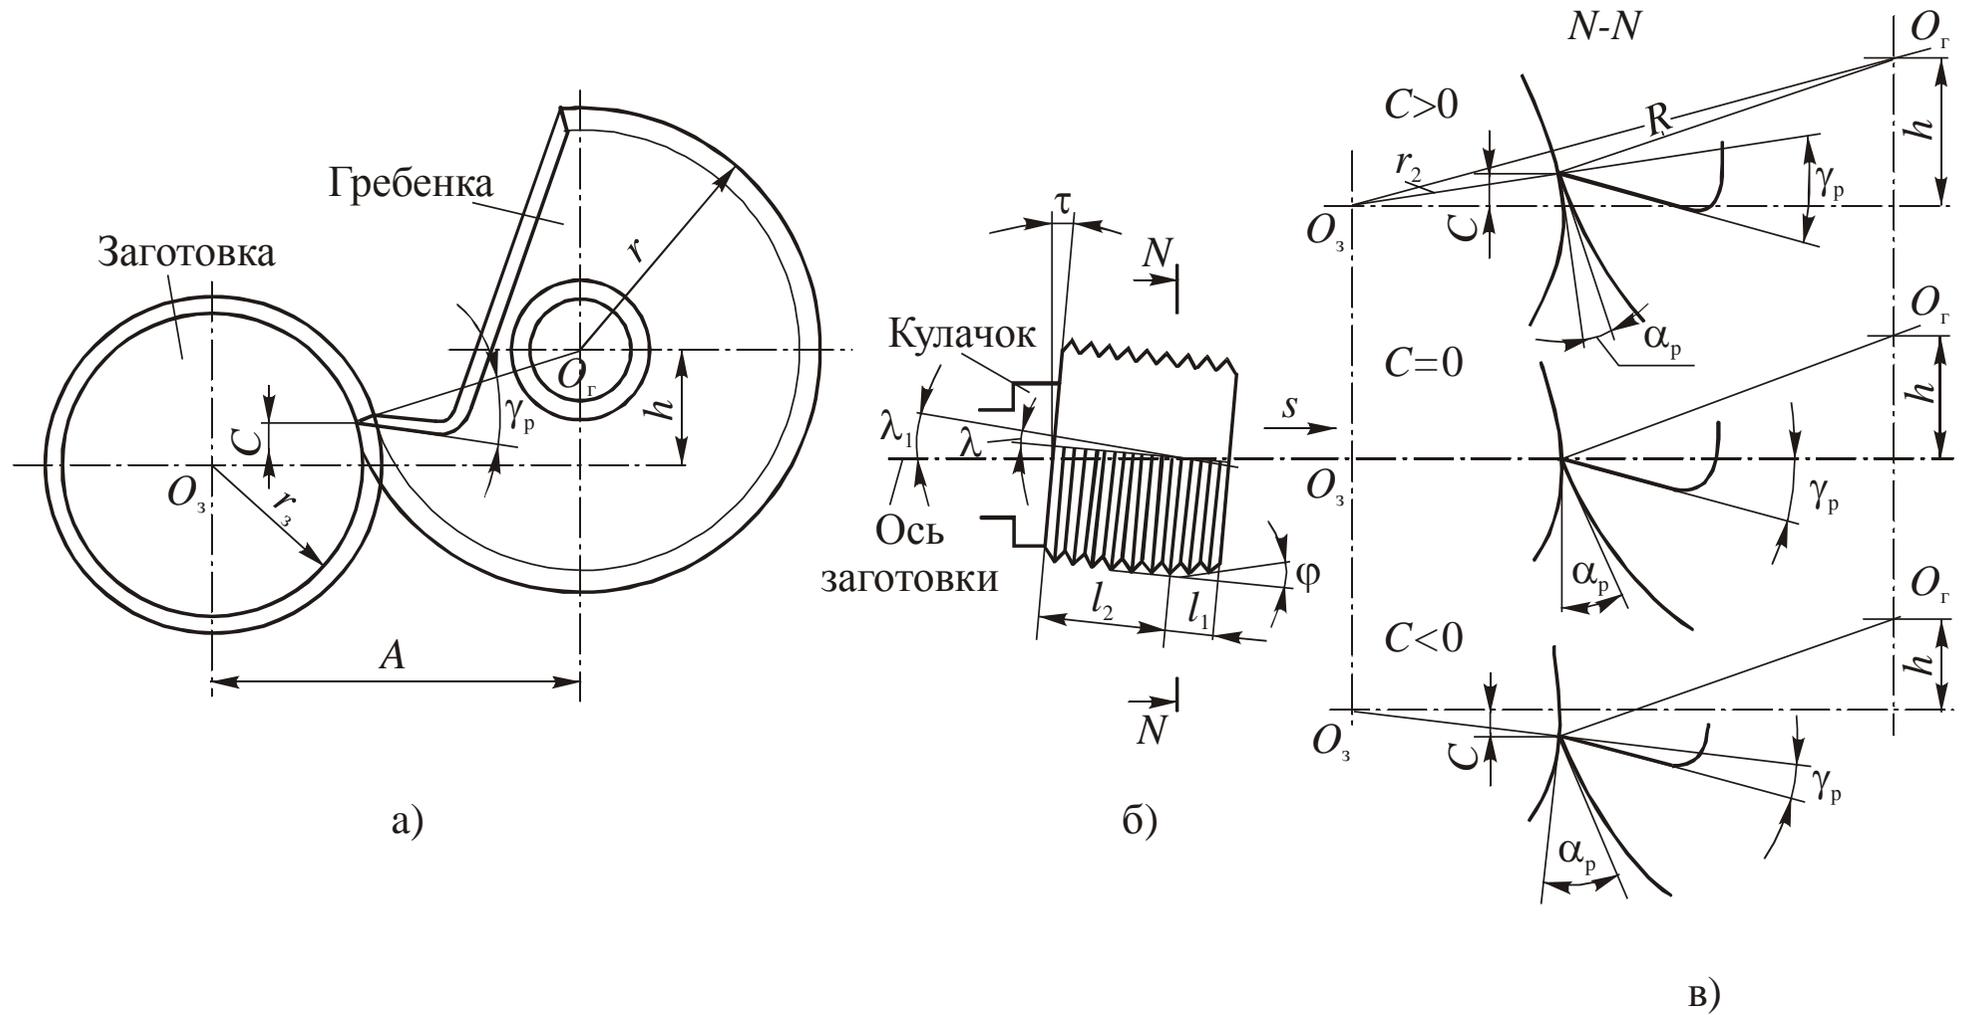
Установка резьбонарезной гребенки относительно заготовки
